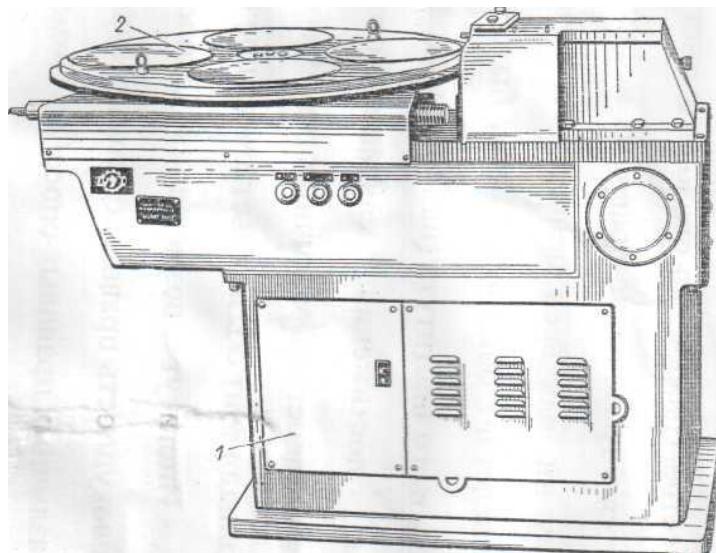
Механизм приготовления круглых фланцев СТД-42
